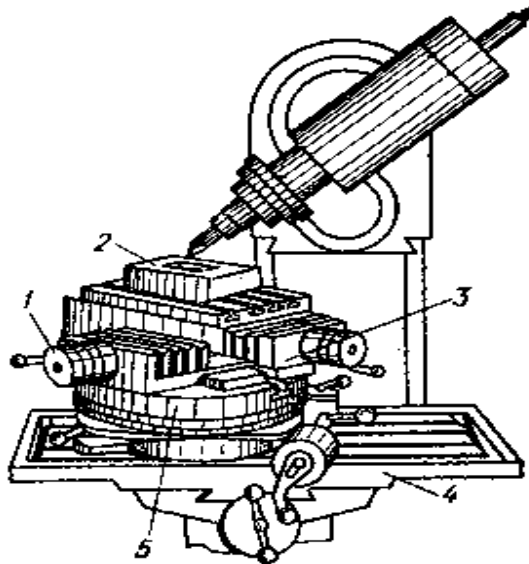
Координатний столик установлений на поворотний стіл вертикально-фрезерного верстата: 1 – лімба; 2 – деталь; 3 – координатний столик; 4 – поздовжній стіл; 5 – поворотний стіл
